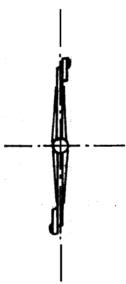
VISTA EN CONJUNTO DEL EJE ROTOR, SOPORTES ASPAS
